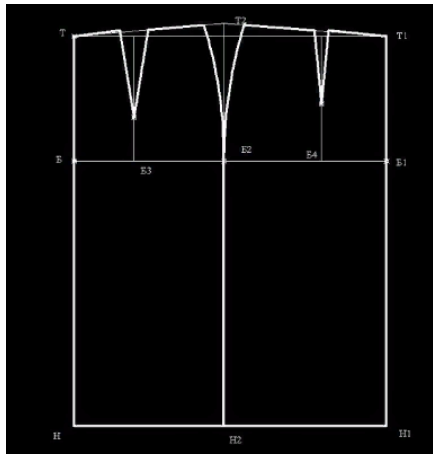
Чертёж базовой конструкции (БК) прямой юбки.
